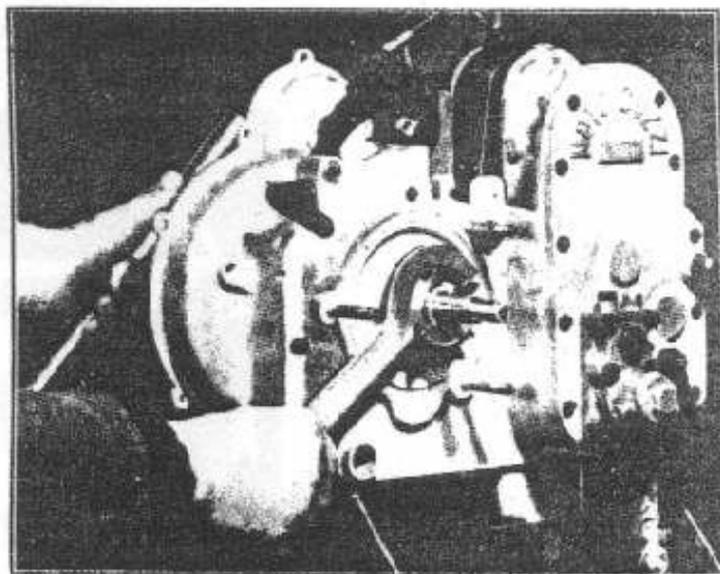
Come si smonta la ghiera di serraggio del pignone del cambio.
